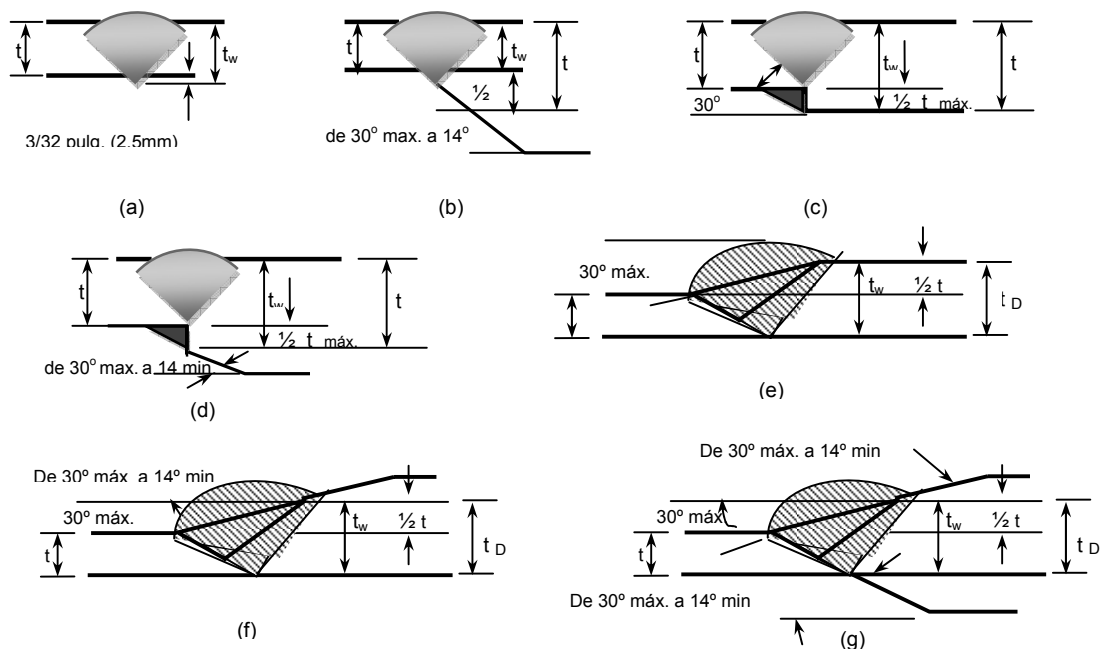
Diseño del bisel en la junta de soldadura para tubos de diferentes espesores de pared [7].
